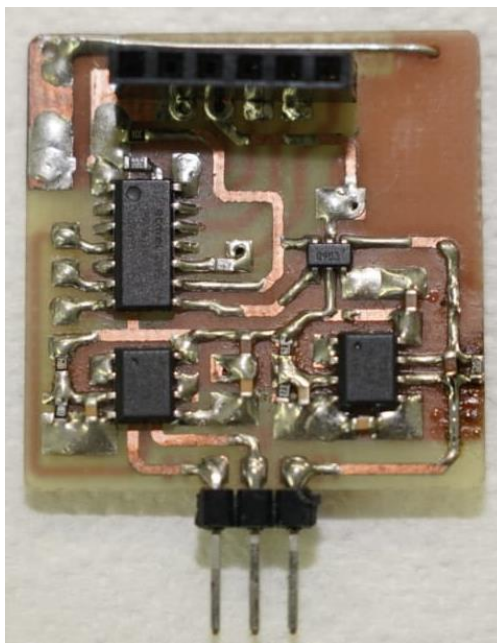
Disseny real de la PCB amb l'ATtiny 1614 i la resta d'elements soldats.
